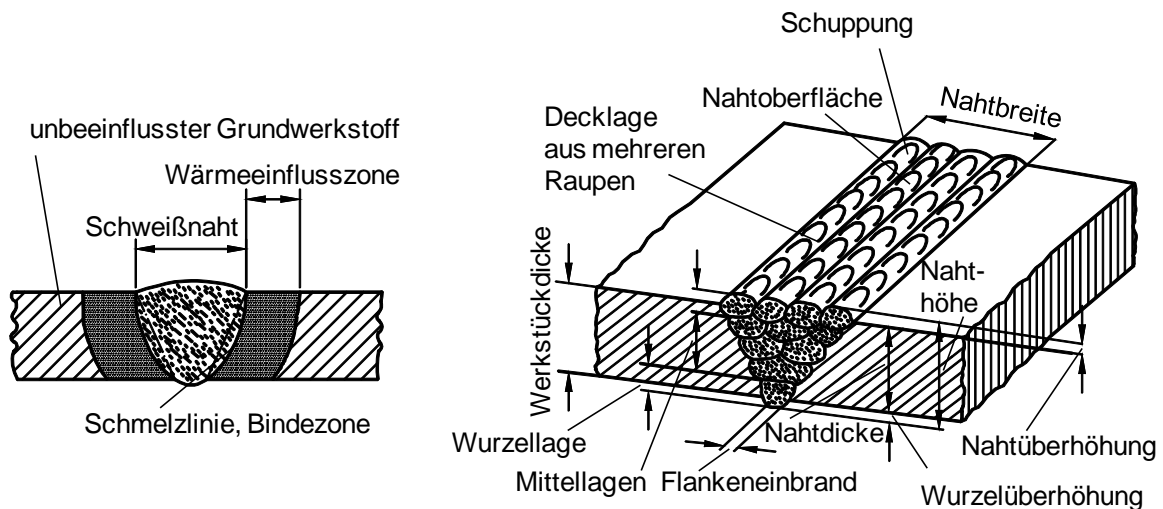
Begriffe und Benennung bei Schweißnähten nach [59]
